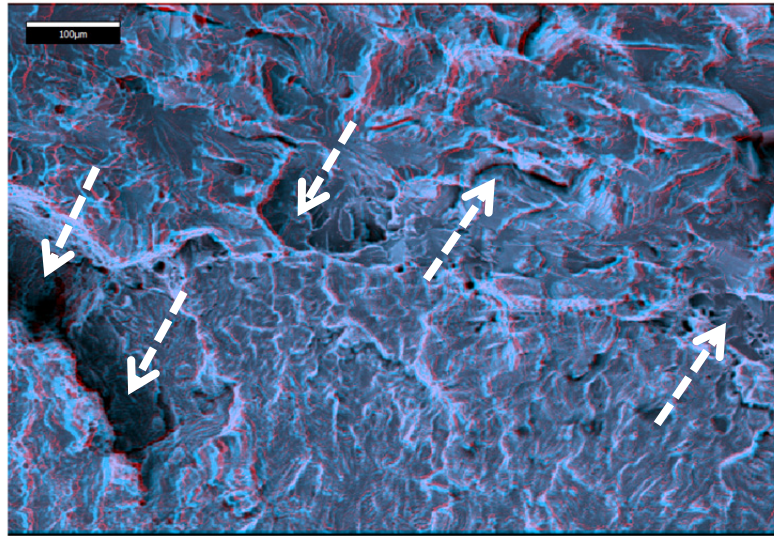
Detailaufnahme Ermüdungsbruch nach $2 \cdot 10^6$ LW (Übergang Ermüdungs- / Restgewaltbruch: strichlierte Pfeile)
